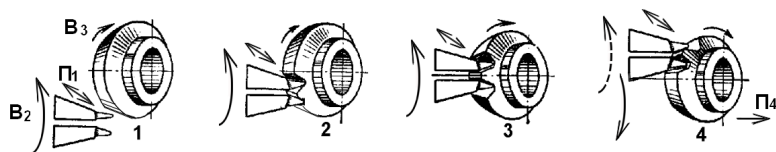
Схема движений: 1 – начало цикла; 2 – резцы начинают снимать стружку; 3 – середина обката; 4 – конец обработки одного зуба: заготовка отводится от инструментов движением Π_4 , движение V_2 реверсируется, а движение заготовки V_3 продолжается в прежнем направлении
